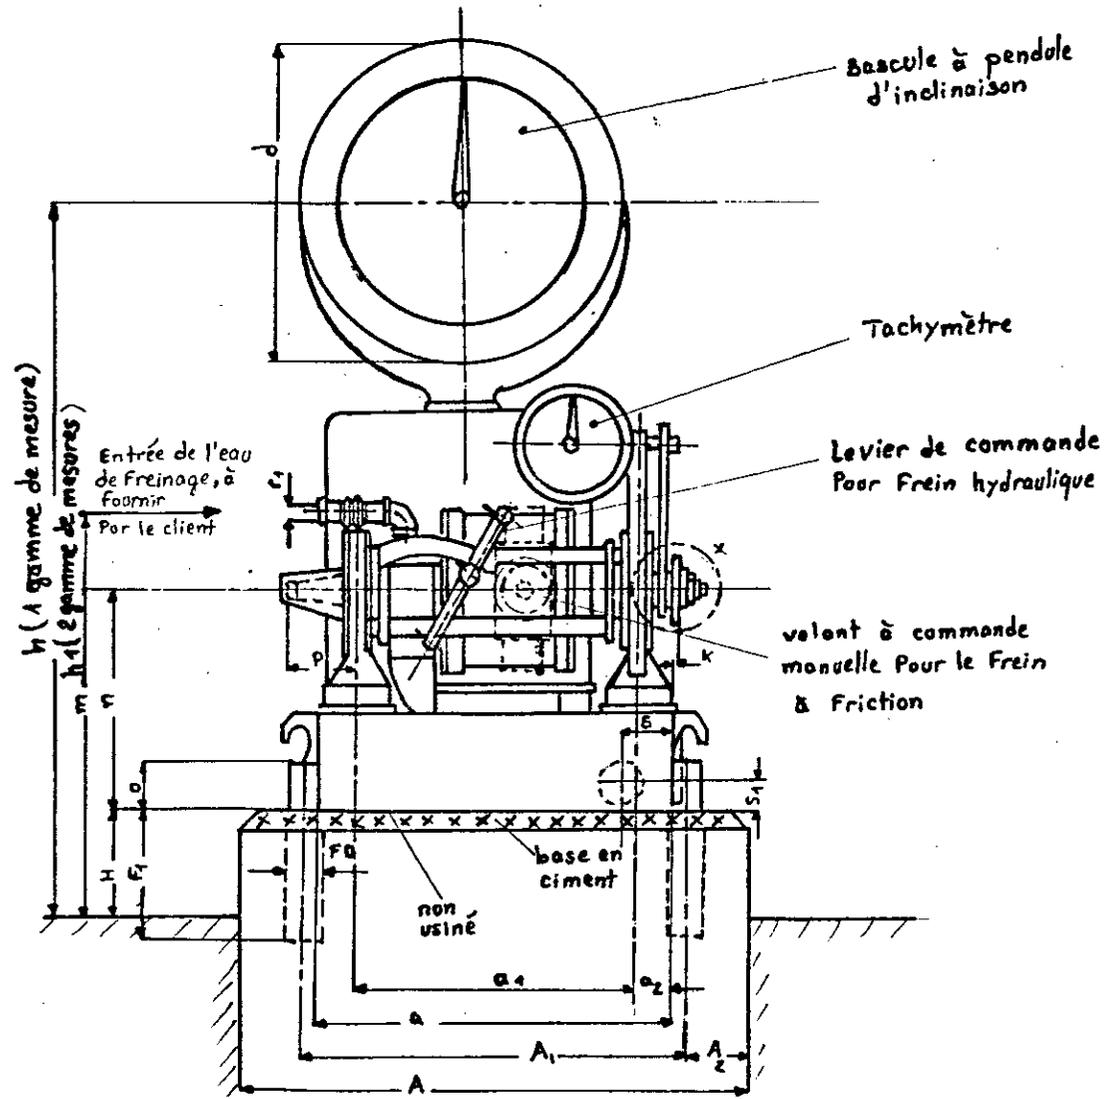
Vue d'ensemble du frein hydraulique SCHENCK
